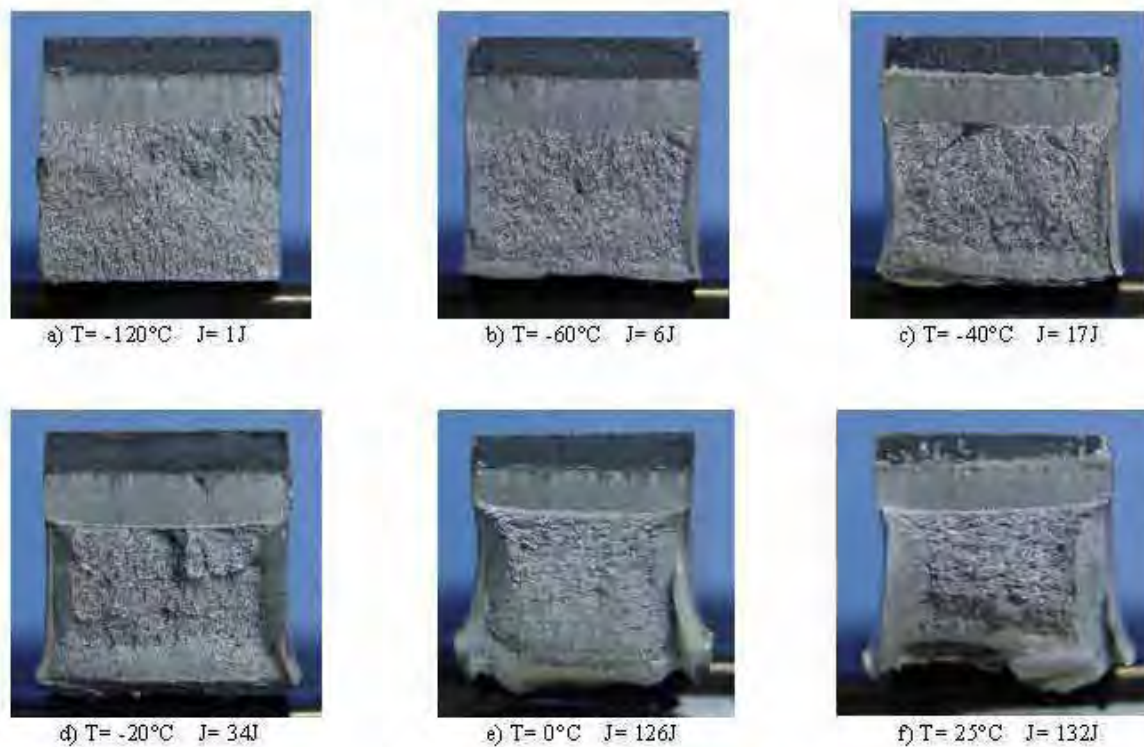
Fractografia da superfície de fratura do aço API - R23 °C/s, corpo-de-prova pré-trincado.
